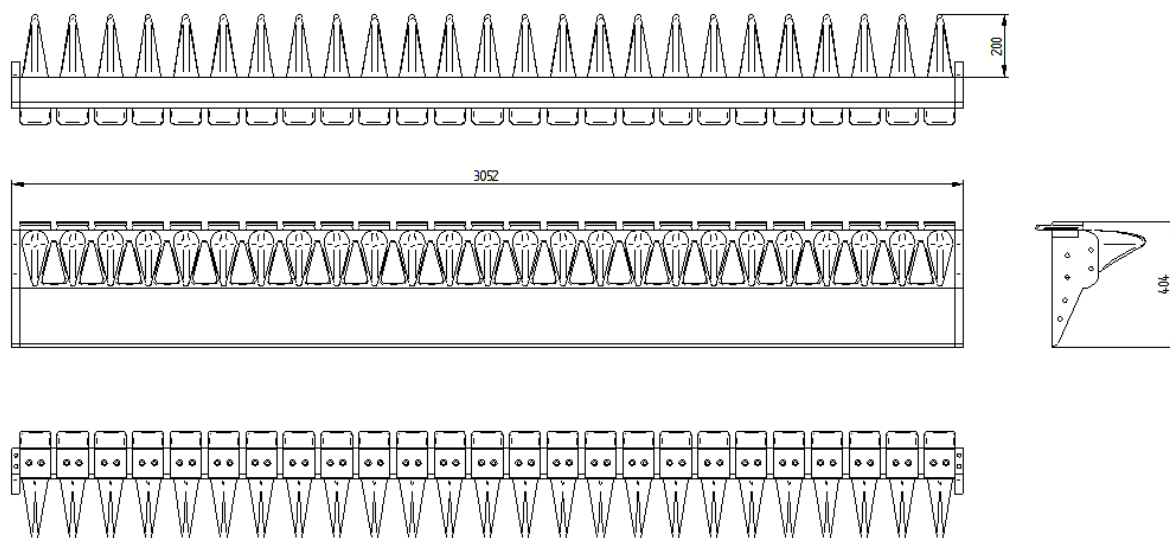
Representação esquemática 2D do Desenho de Conjunto do Raspador (dimensões em mm).
